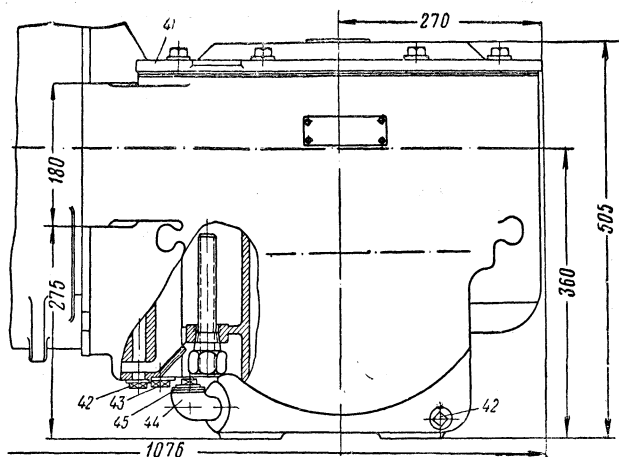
Мотор-компрессор усл. № Э-400 (внешний вид)
